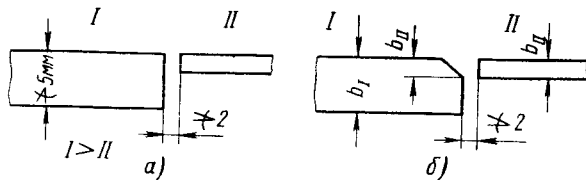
Разделка кромок при сварке различной толщины детали
